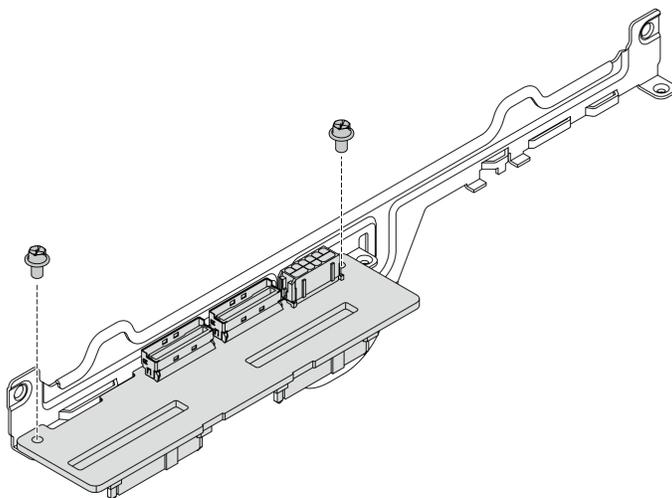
Installation du fond de panier d'unité 2,5 pouces au module
